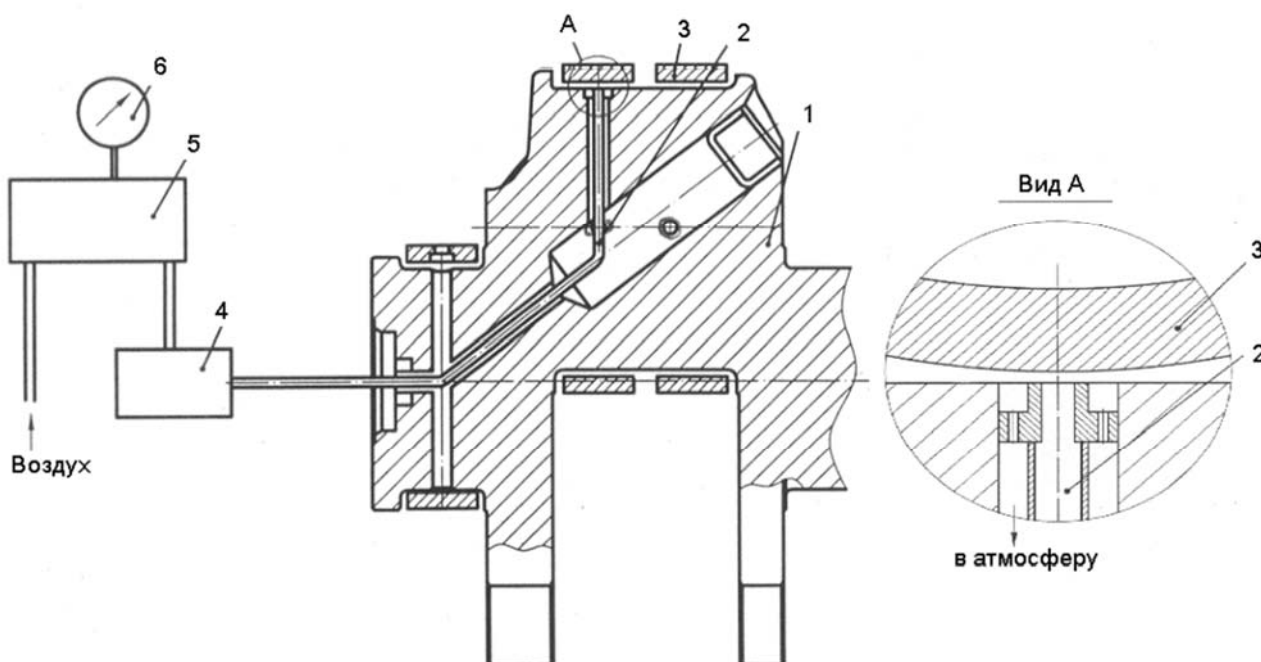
Схема определения зазора в шатунном подшипнике двигателя КАМАЗ 740: 1 – коленчатый вал; 2 – трубки подвода воздуха к жиклерам; 3 – шатунный вкладыш; 4 – переходная муфта; 5 – узел подготовки воздуха; 6 – электронное измерительное устройство
